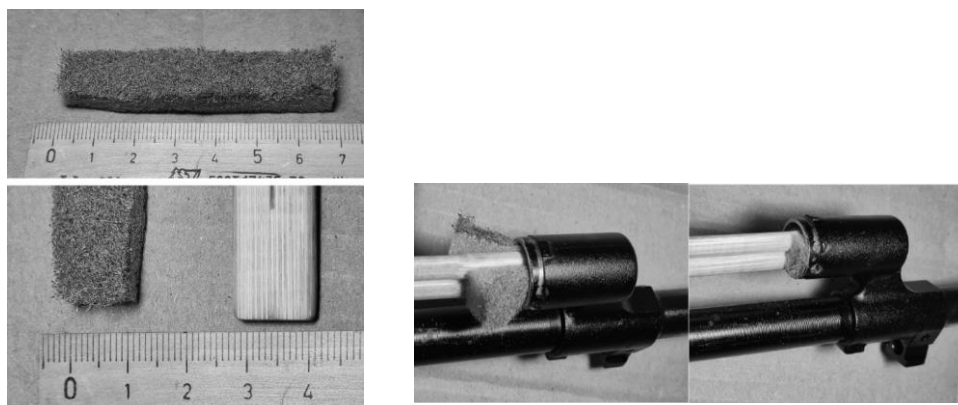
Подготовка абразивной губки и палочки для чистки газовой камеры (патрубка камеры)
